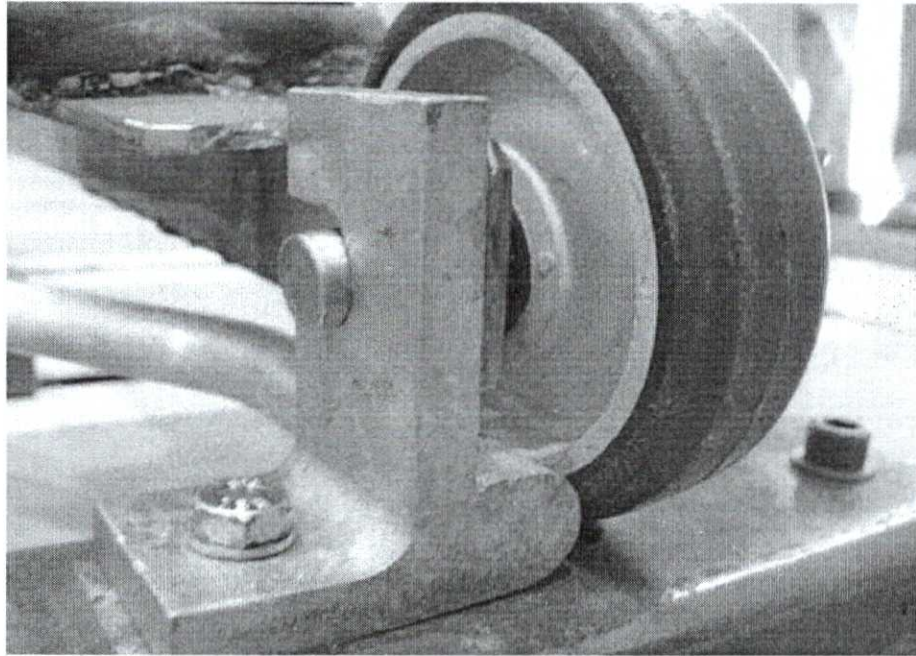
Lado esquerdo da amostra 3 após ensaio.
